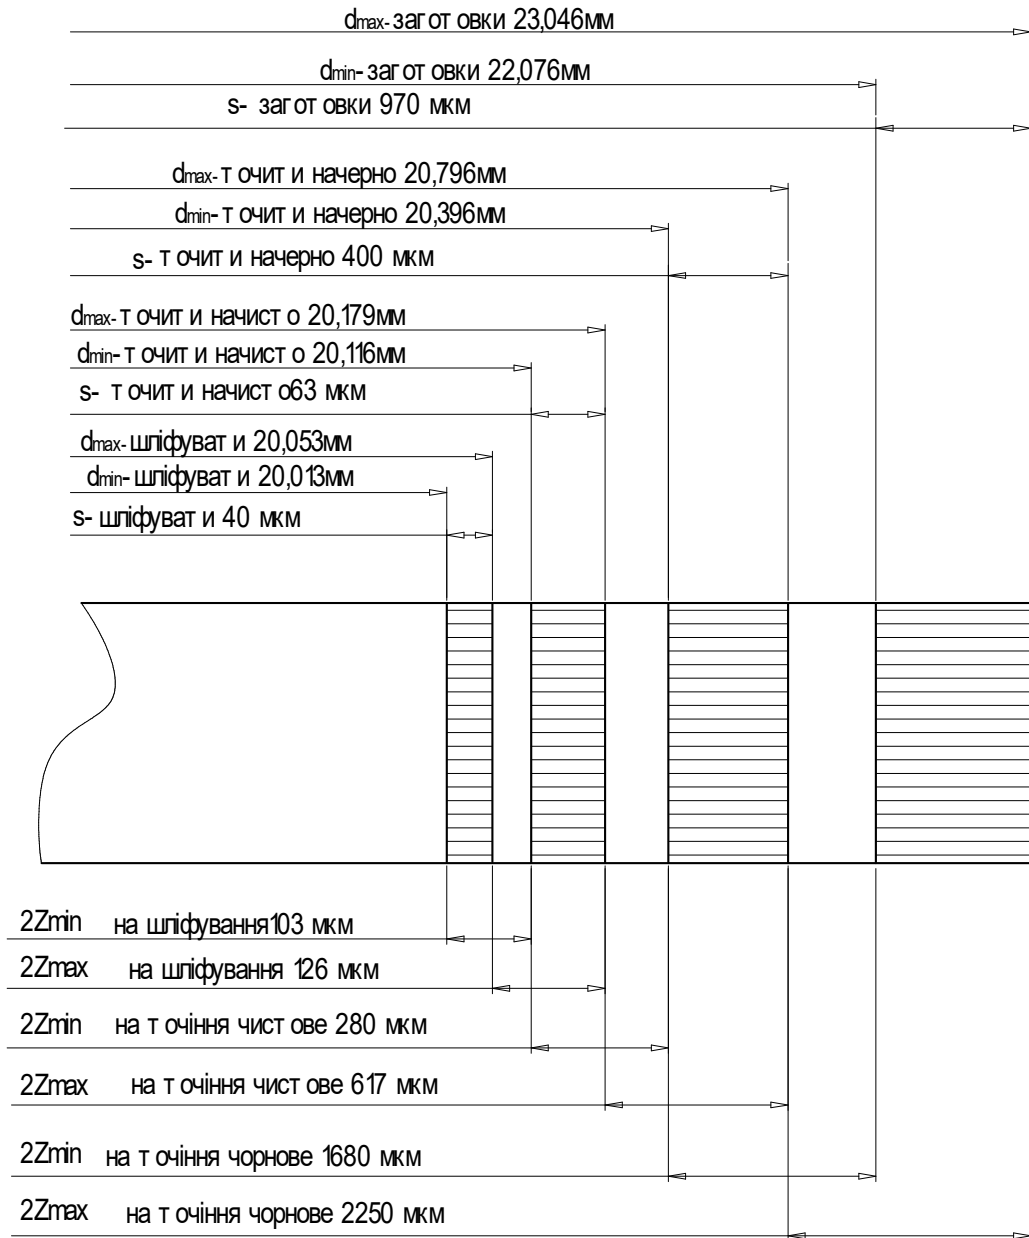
Схема розміщення припусків приобробленні поверхні $\varnothing 20h6$
